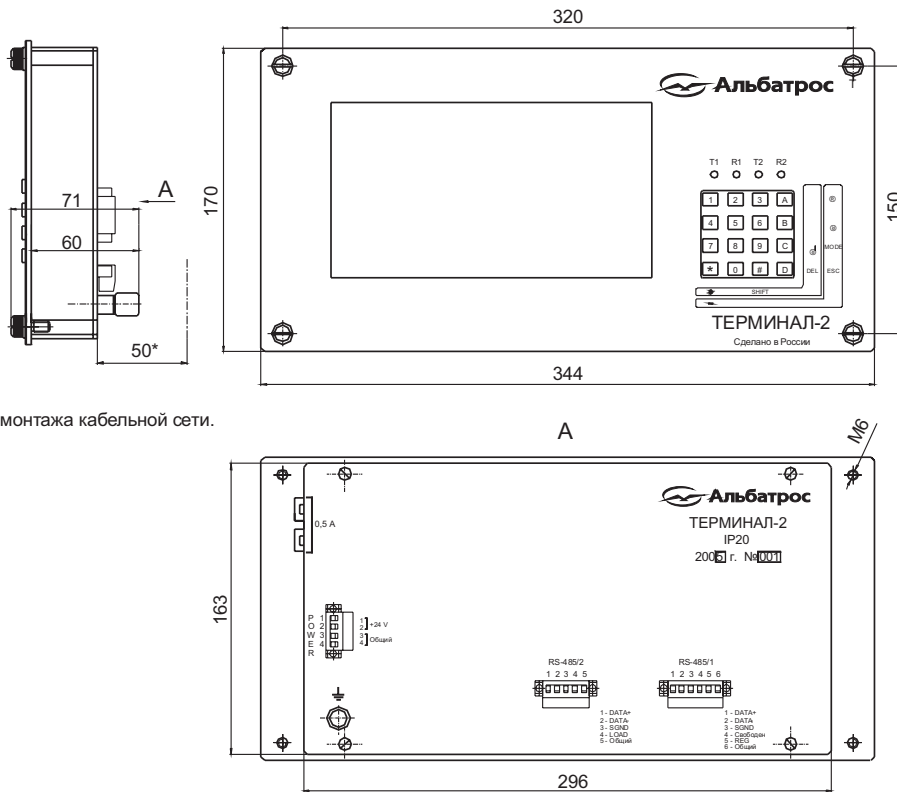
Внешний вид и габаритные размеры Терминала
